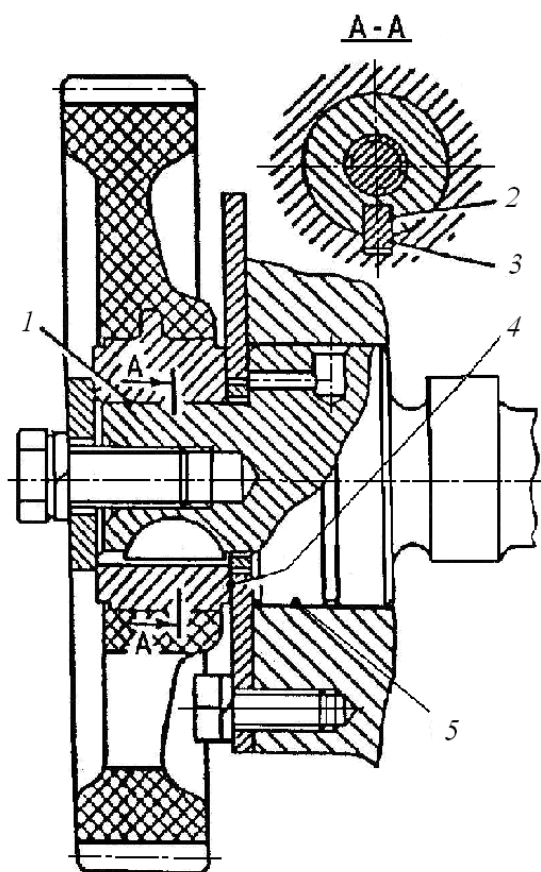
Привод распределительного вала двигателя автомобиля «Газель»
